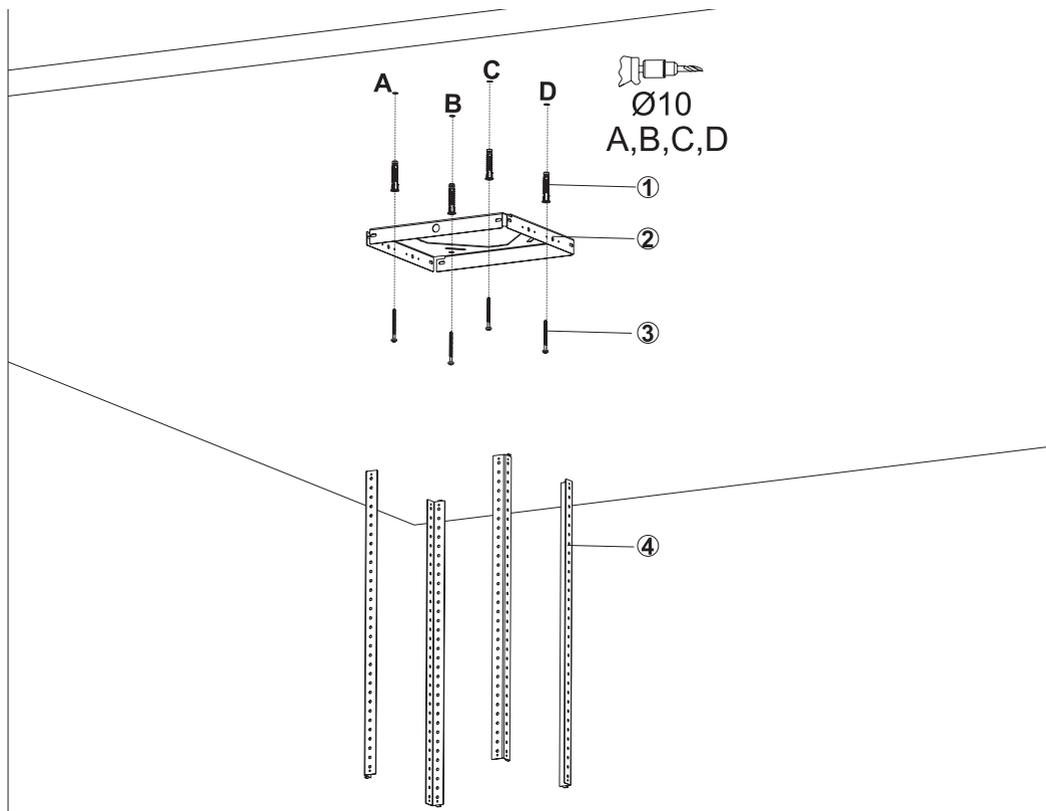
INSTALLAZIONE E COMPONENTI PARTE 1
